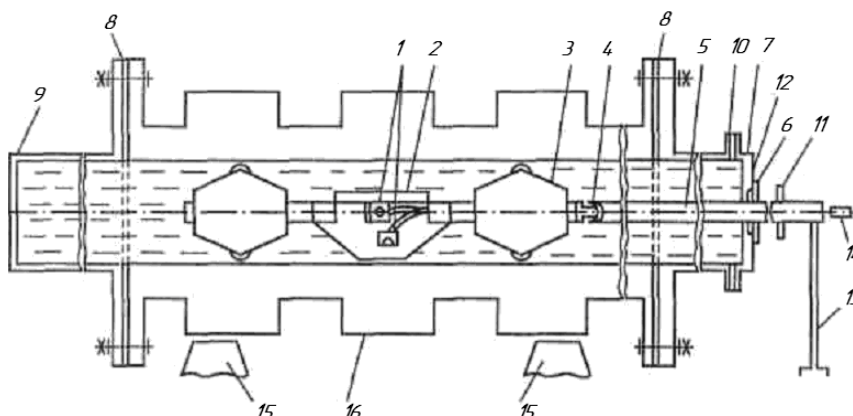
Общий вид устройства для ультразвукового контроля ротора иммерсионным методом: 1 – пьезоэлектродпреобразователь; 2 – каретка; 3 – центратор; 4 – шарнир; 5 – штанга; 6 – резиновая манжета; 7 – проходное доньшко; 8 – резиновые прокладки; 9 – глухое доньшко; 10 – патрубок; 11 – рукоятка подачи; 12 – азимутальный диск; 13 – тренога; 14 – кабель к дефектоскопам; 15 – опоры; 16 – ротор
